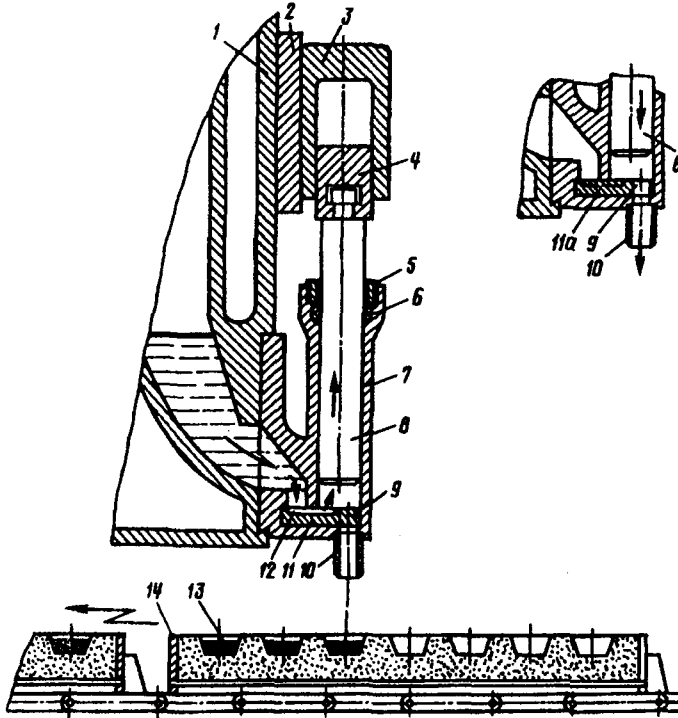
Схема дозирующего устройства отливочного механизма
